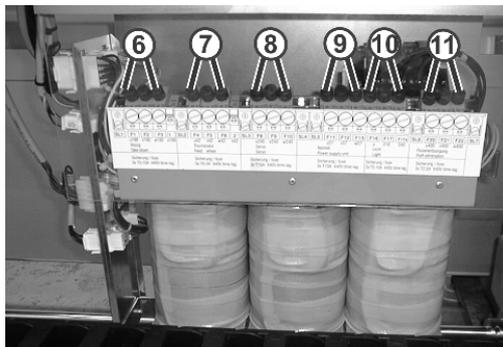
Fusibles del transformador en la parte posterior de la máquina
